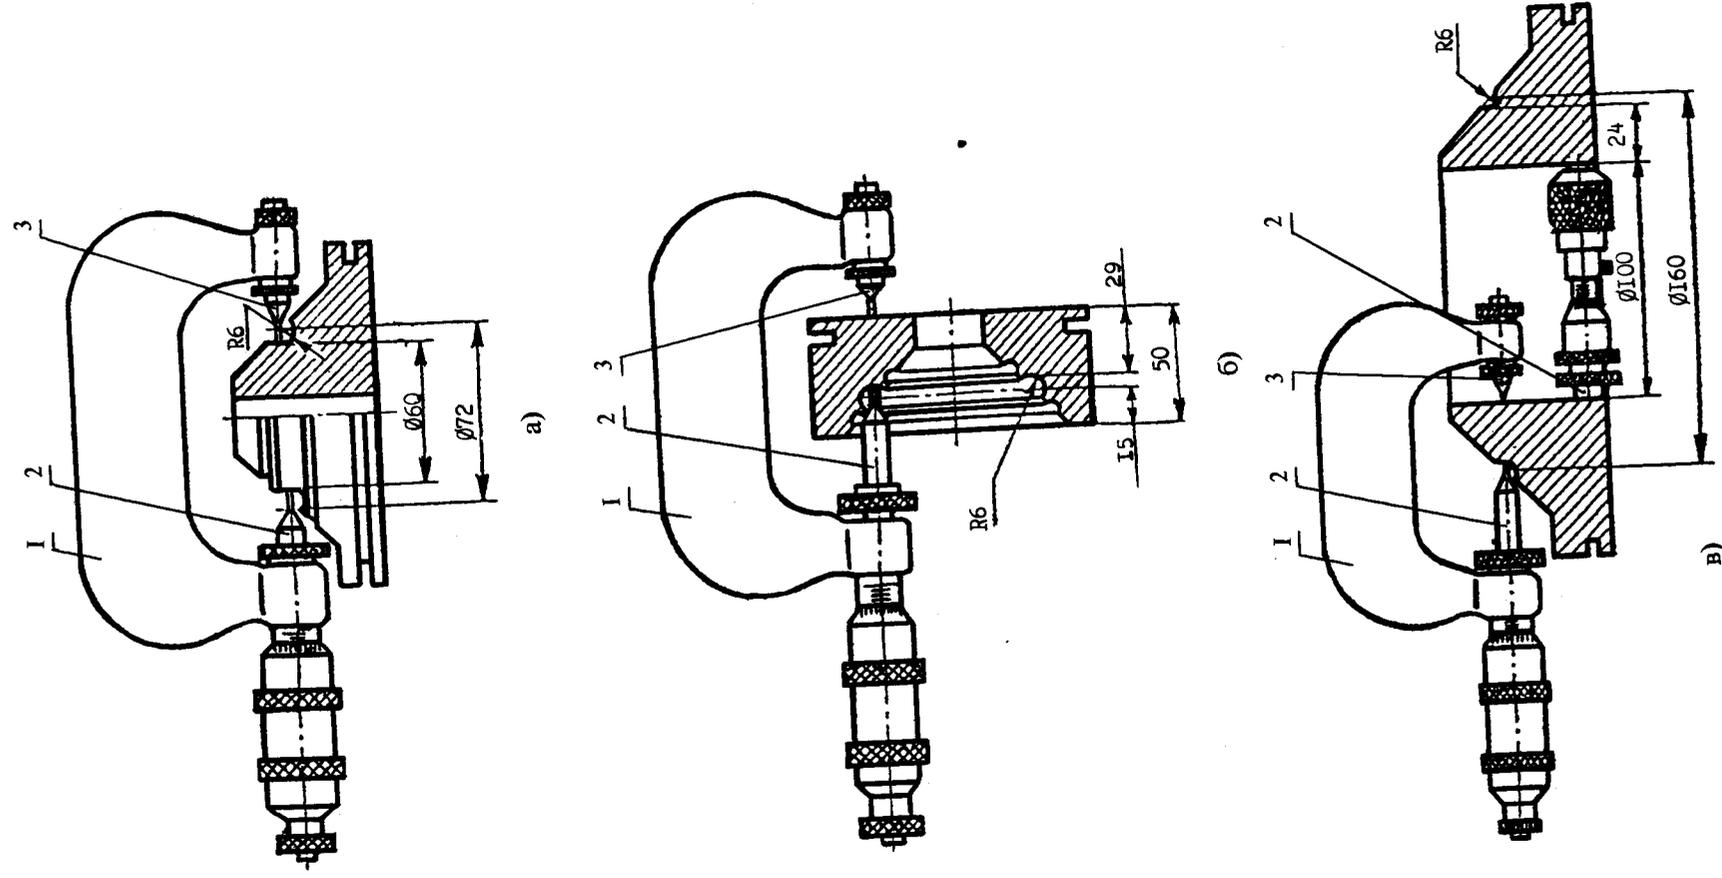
Приспособления - вставки для контроля формирующих гнезд в пресс - формах:
